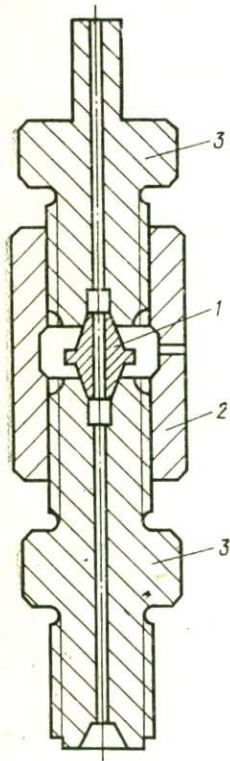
Затвор типа «чечевица». 1 — чечевица, 2 — стягивающая гайка с правой и левой резьбой, 3 — корпусы стягиваемых деталей (Циклис, 1976)
